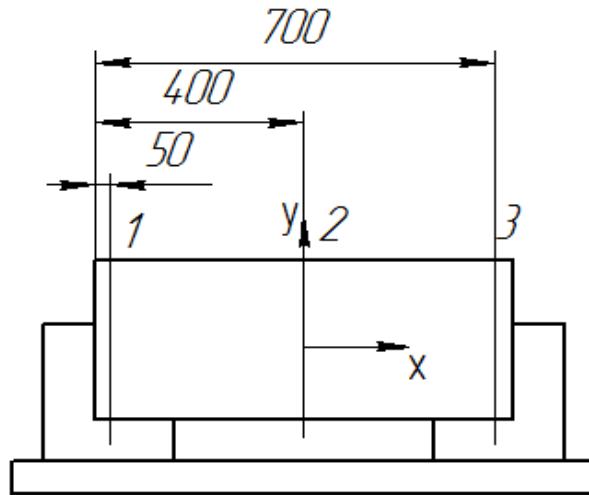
Розрахункова схема досліджуваної заготовки
